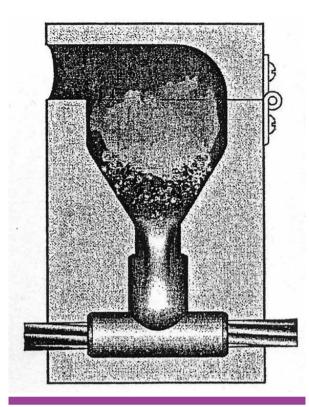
Fin de la colada y formación de la soldadura
